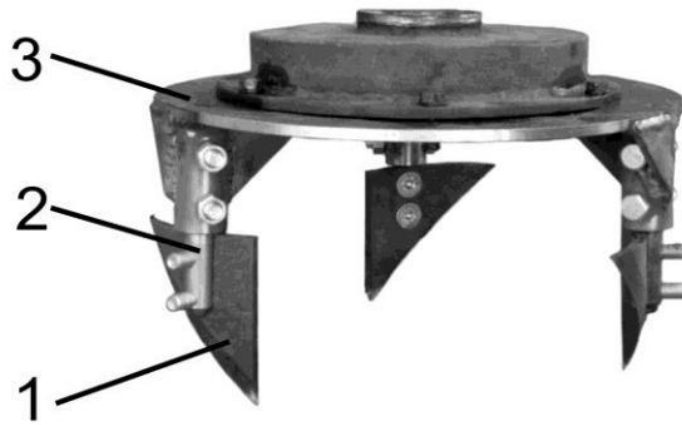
Ротор (ножовий) фрезмашини: 1 - ніж; 2 - стійка ножа; 3 - диск.
